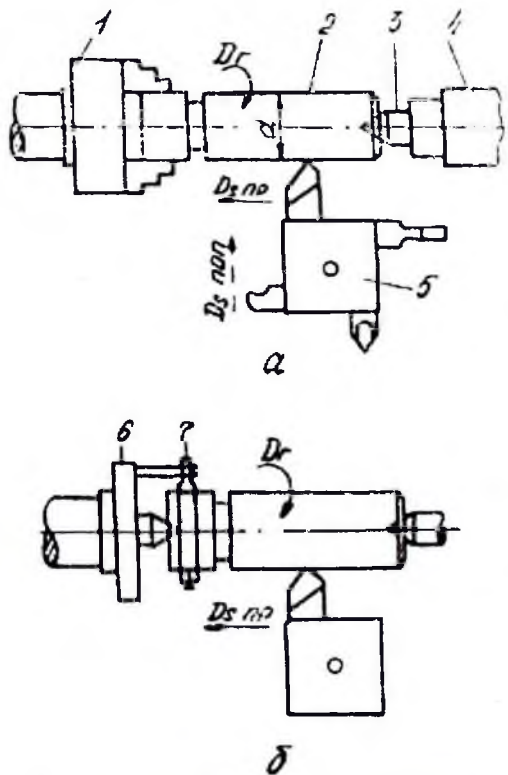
Схема токарной обработки и рабочие движения при закреплении заготовки в патроне (а) и в центрах (б)
